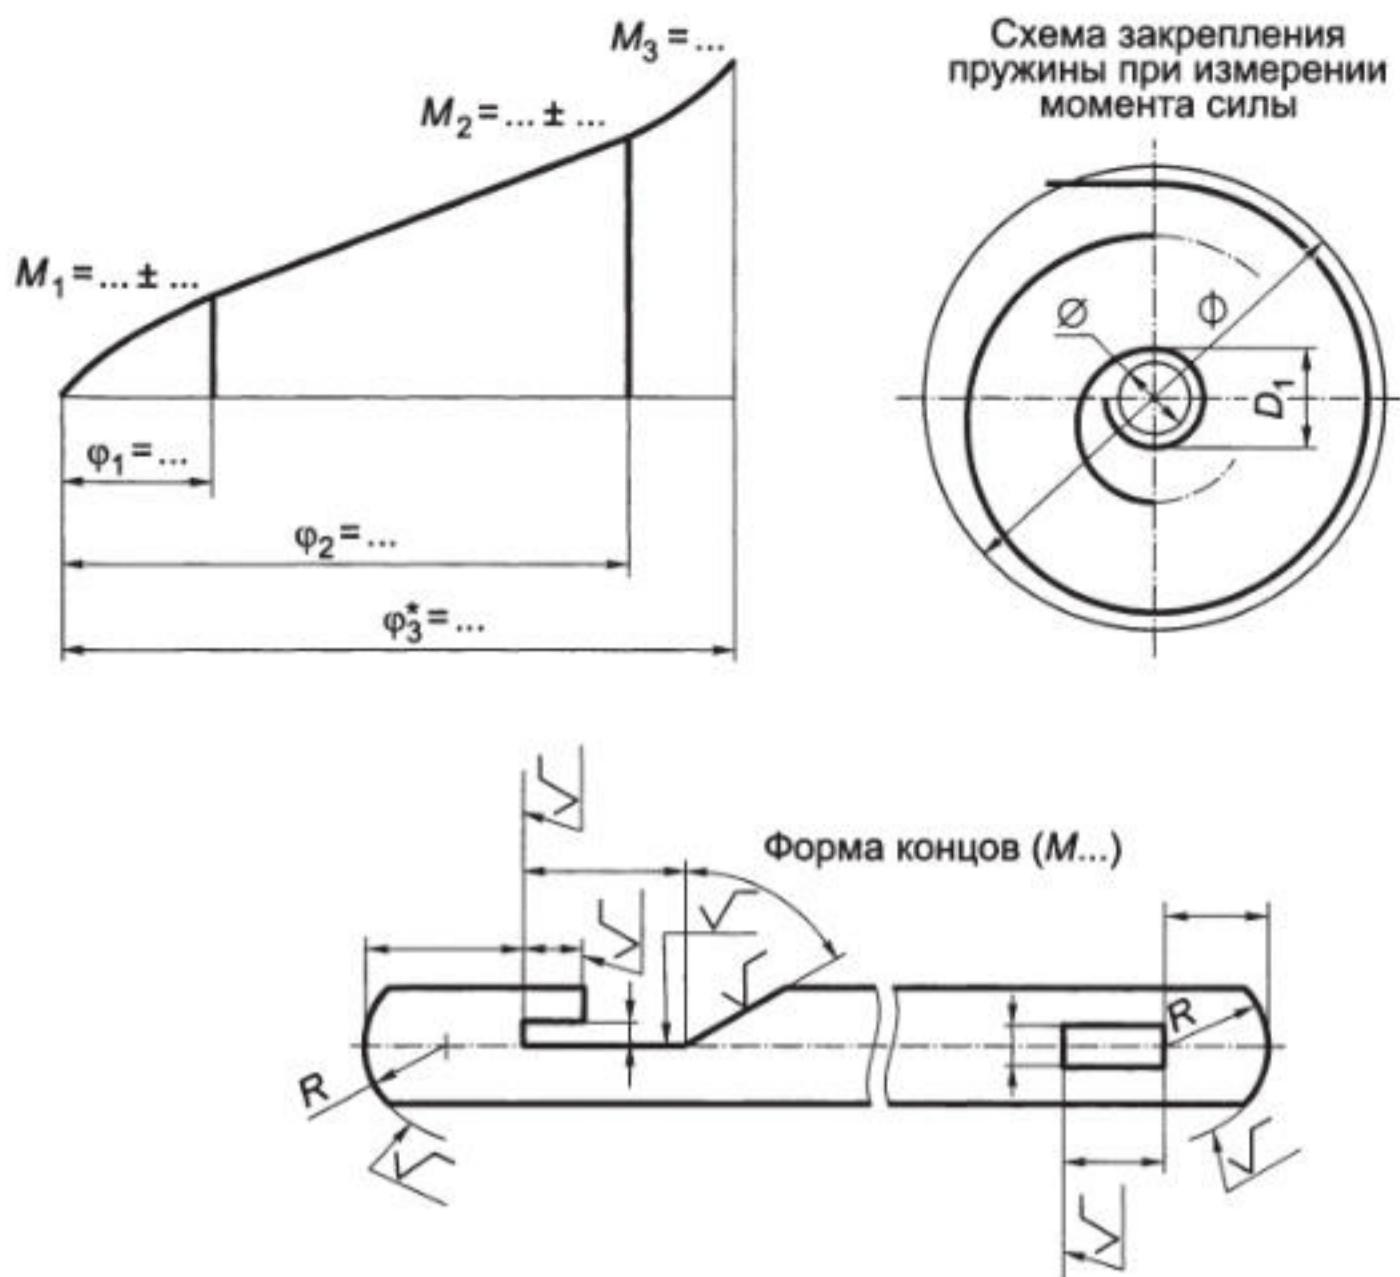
Пружина спиральная плоская из заготовки прямоугольного сечения с креплением к валу и барабану
